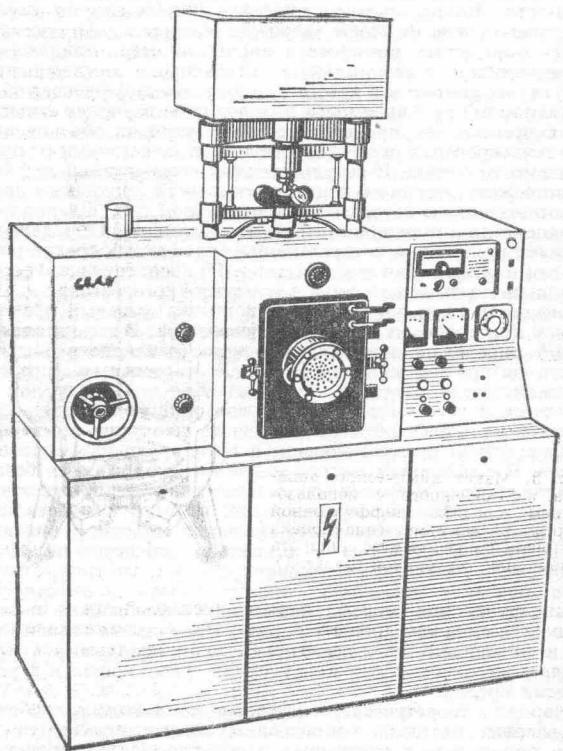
Установка диффузионной сварки в вакууме, сконструированная и изготовленная в проблемной научно-исследовательской лаборатории диффузионной сварки в вакууме МАТИ.
